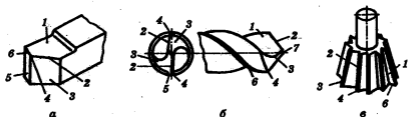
Рабочие поверхности и режущие кромки резца (а), сверла (б), фрезы (в)
